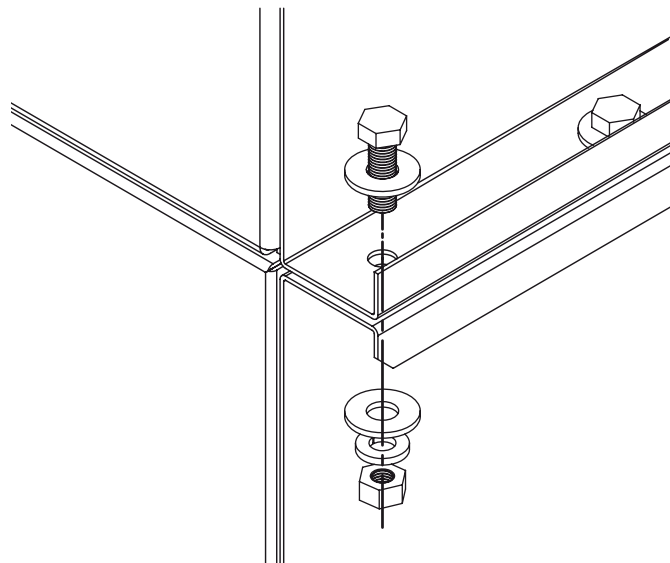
Details Zusammenbau Ausblashaube oder Schalldämpfer
